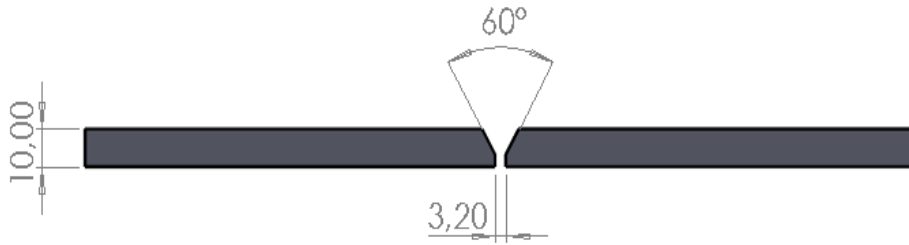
Bisel y espaciamento de la probeta de doblado utilizado para la soldadura en V (Unidades en mm) utilizando SolidWorks.
